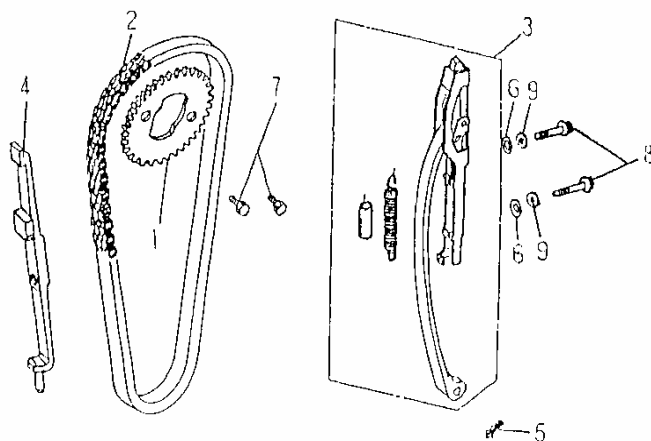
CAM CHAIN.TENSIONER 內鏈條.拉力桿
